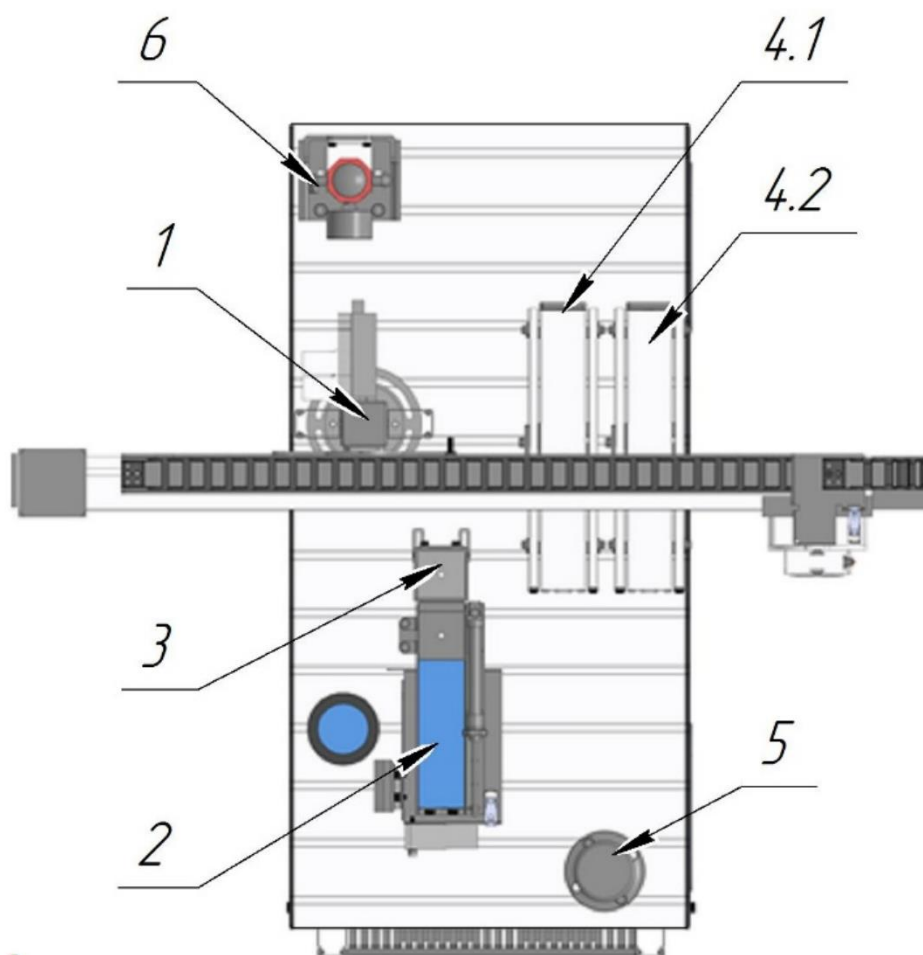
Конструкция мехатронной станции (вид сверху):
